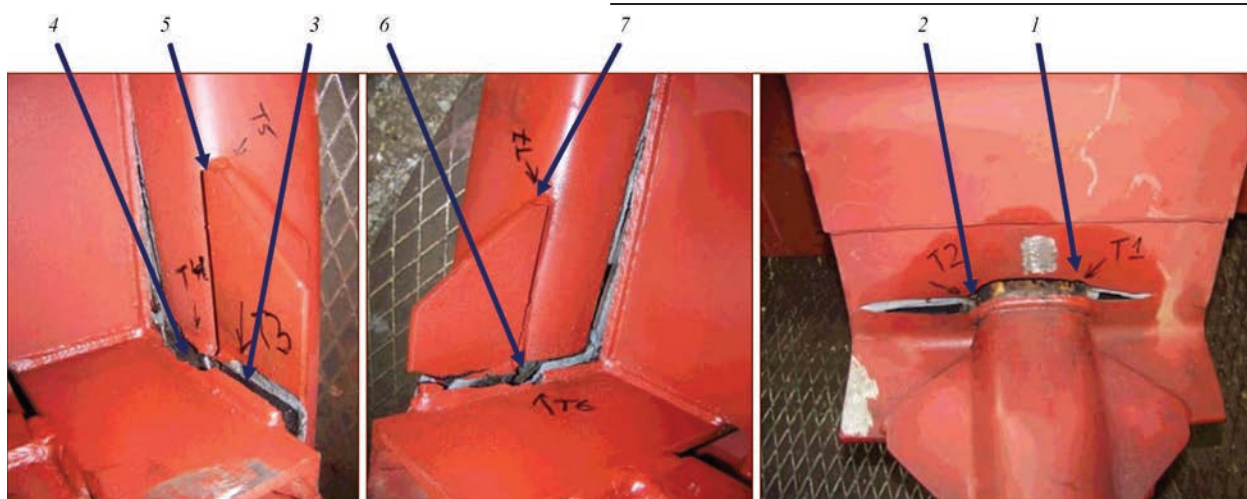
Трещины в узле заделки стойки боковой стены (образец № 4): 1, 2 — в соединении поперечной балки (накладки над верхней полкой) с нижней обвязкой (трещины T1 и T2, соответственно); 3 — в соединении усиливающего уголка стойки боковой стены с нижней обвязкой (трещины T3); 4, 6 — в соединении стойки боковой стены с нижней обвязкой (трещины T4 и T6, соответственно); 5, 7 — вверху усиливающего уголка стойки боковой стены (трещины T5 и T7, соответственно)
